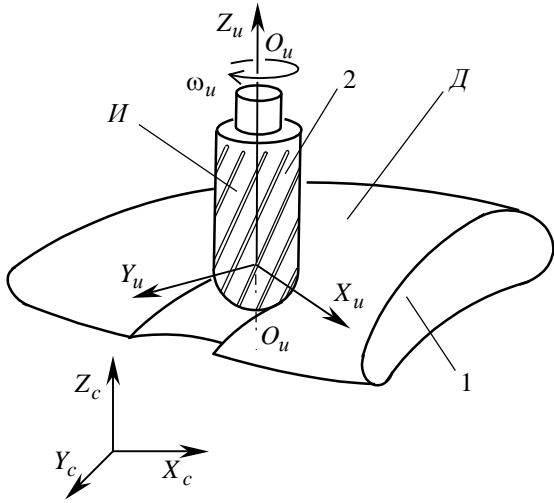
Схема способа обработки сложной поверхности детали с переменной подачей инструмента вдоль строки формообразования
